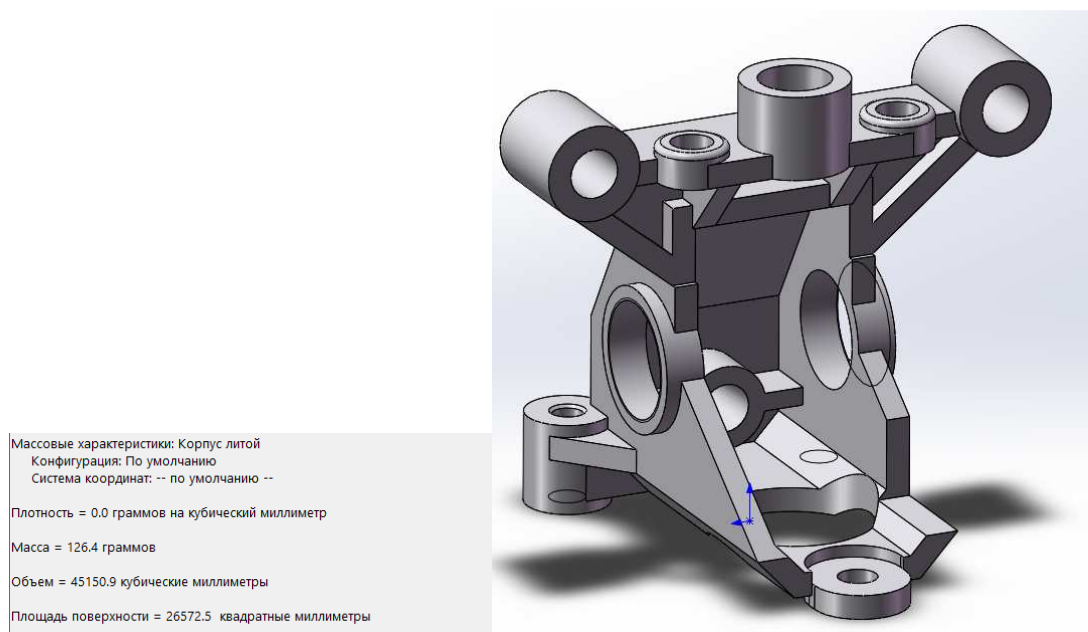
Загальний вигляд 3D-моделі деталі
